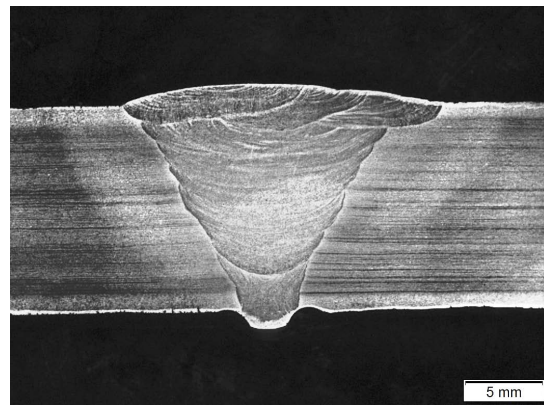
Probe G03-03, Schweißnaht FAT 112, Riss in der Schweißnaht, Beginn an einem Schlackeeinschluss
